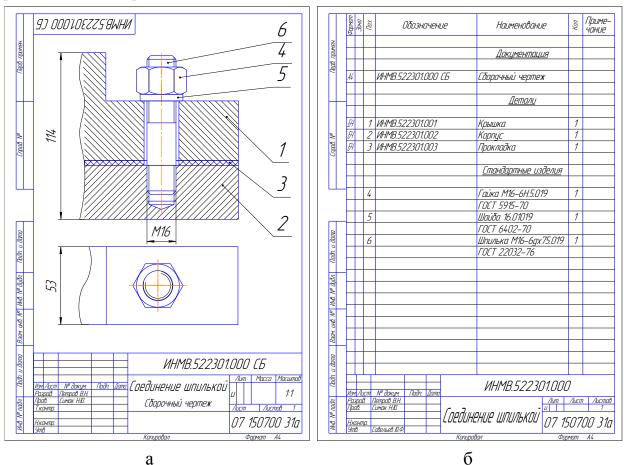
Соединение шпилькой: а – сборочный чертеж, б – спецификация
